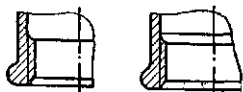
Варианты конструктивного исполнения деталей с внутренней резьбой
